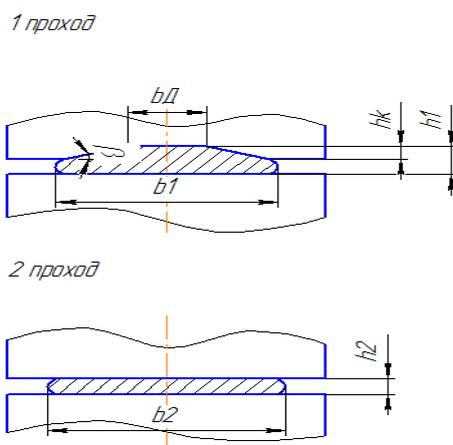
Прокатка рессорной заготовки в два прохода
